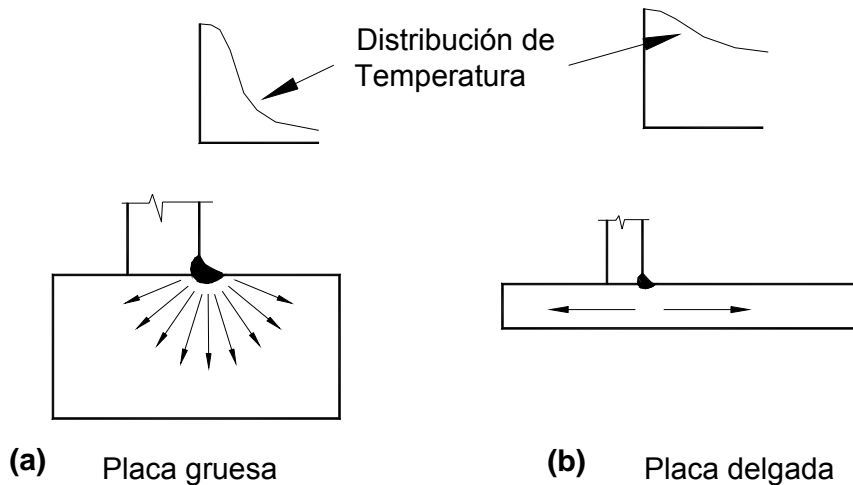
Sección transversal de soldadura.
